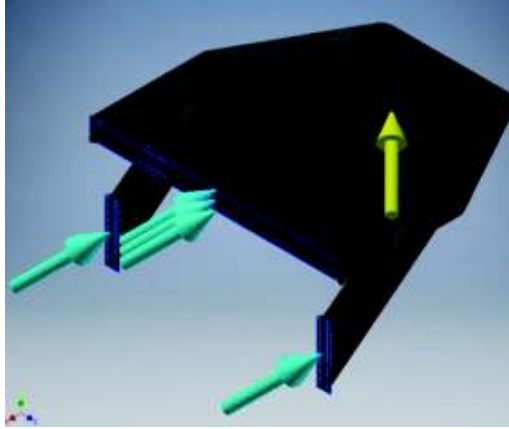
Cargas y restricciones sobre la placa de elevación.
